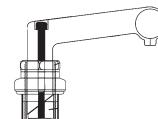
Конструкция резьбовой рулевой колонки и регулировка положения руля
